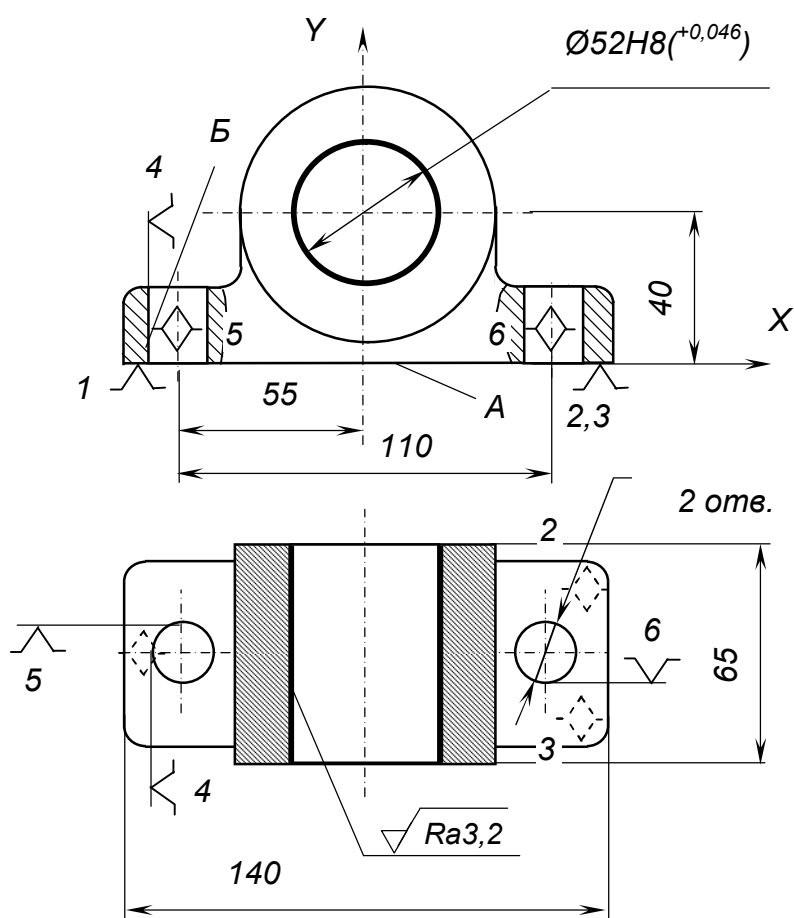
Ескіз зі схемою базування на операції обробки отвору в заготовці деталі типу «корпус»
